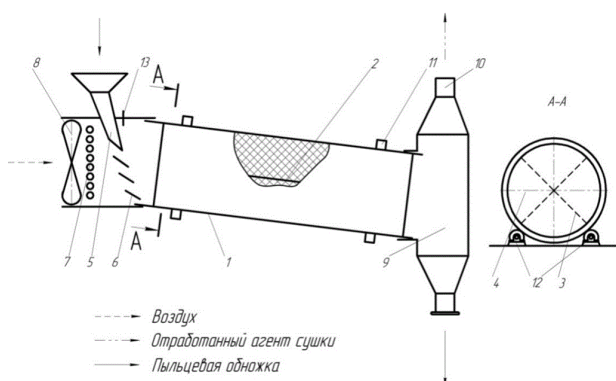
Конструктивно-технологическая схема сушилки пыльцевой обложки и перги
